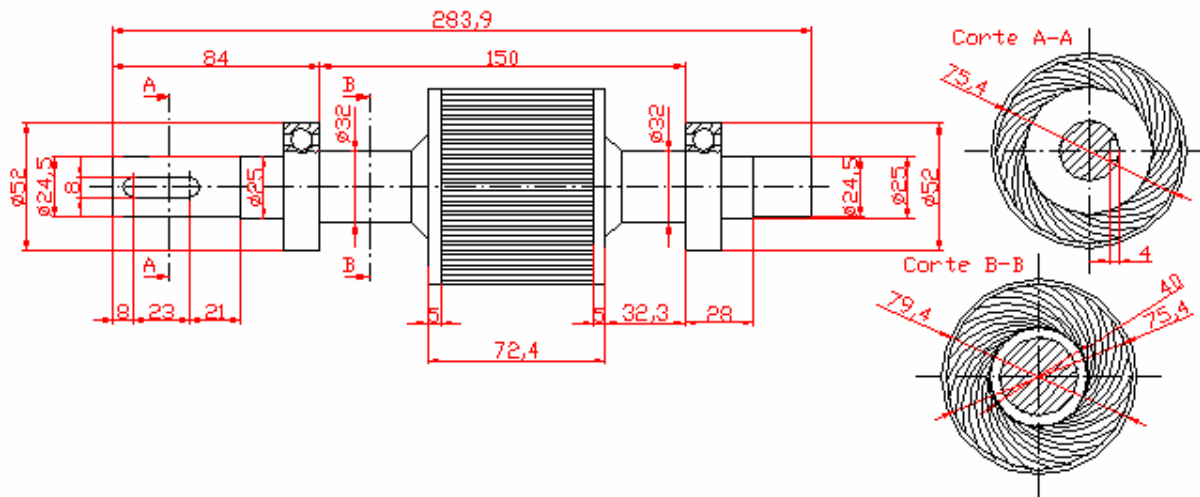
Vista lateral y en planta del rotor de chapas tipo C. Las cotas están dadas en mm.
